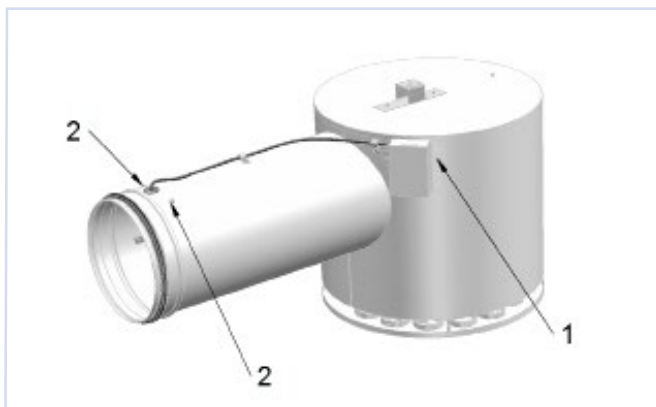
, Skruva av kretskortslocket (1). Koppla sedan från motorledningarna på kretskortet. Lossa de båda skruvarna till motorfästet på stosen (2). (Skruva direkt på motorn på dimension 125) Avlägsna därefter fronten. (MI)
